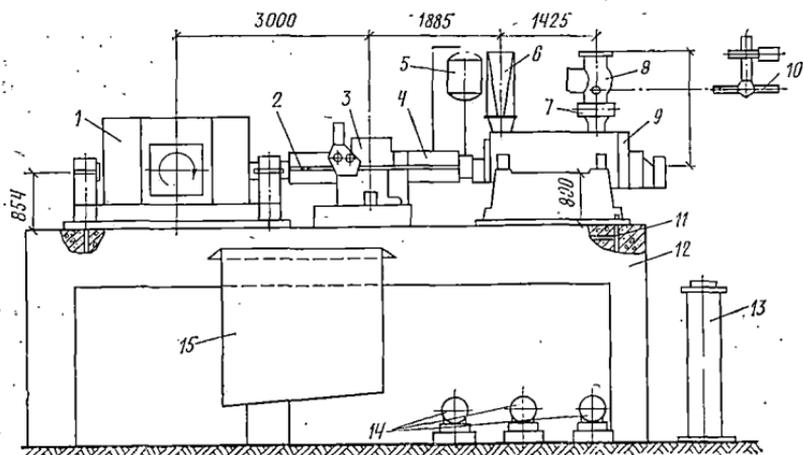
Установочный чертеж насосного агрегата типа ПЭ с гидромuftой
